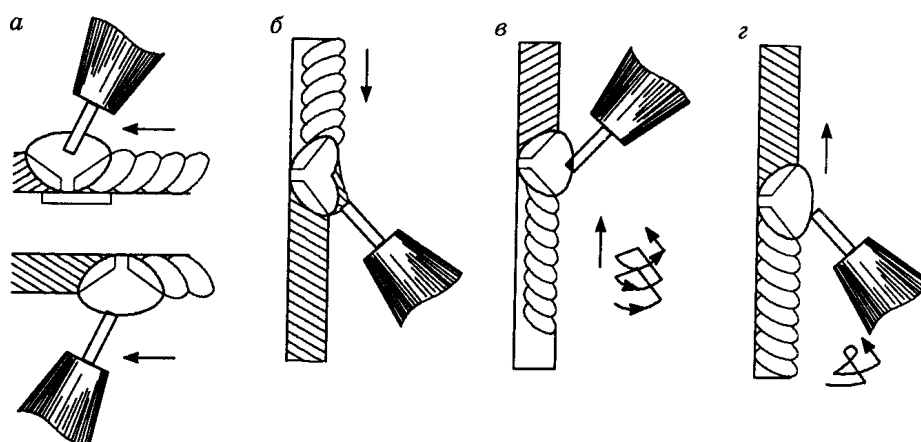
Схемы расположения и поперечные колебания электрода при полуавтоматической сварке в углекислом газе
